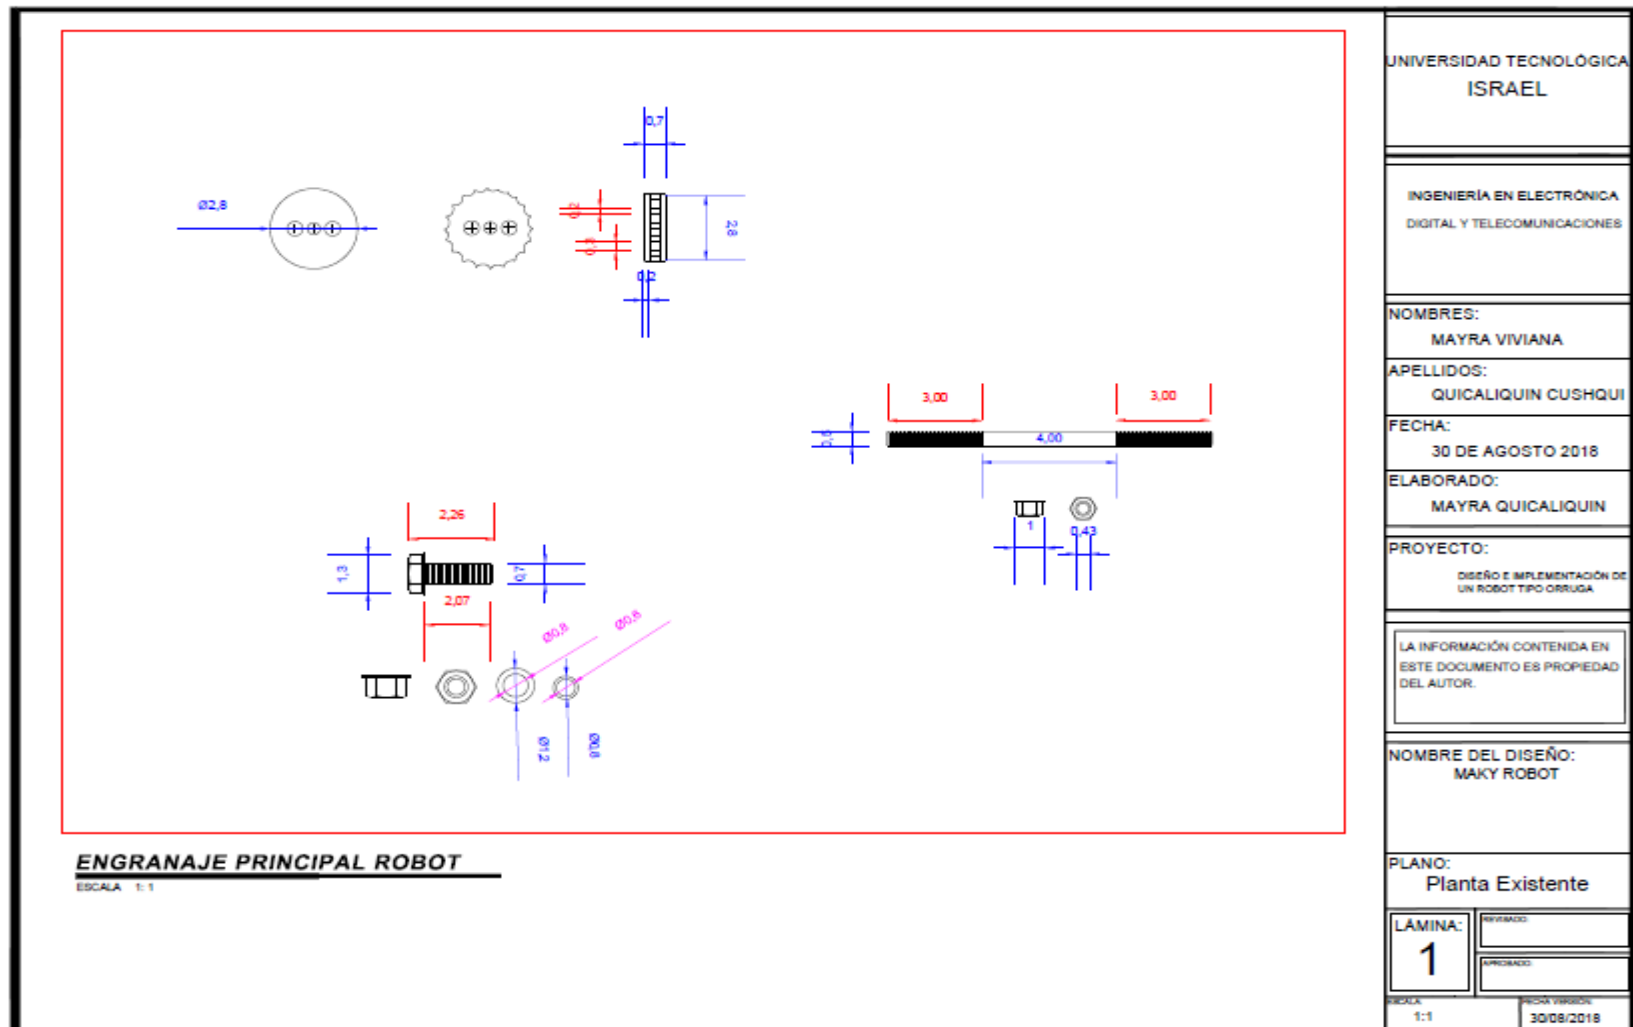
Vista frontal y lateral del engranaje, sujetador y pernos M3
